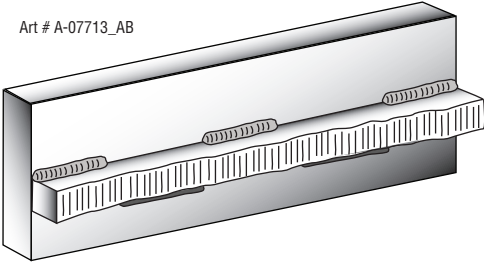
Soldadura discontinua con cordones no paralelos
